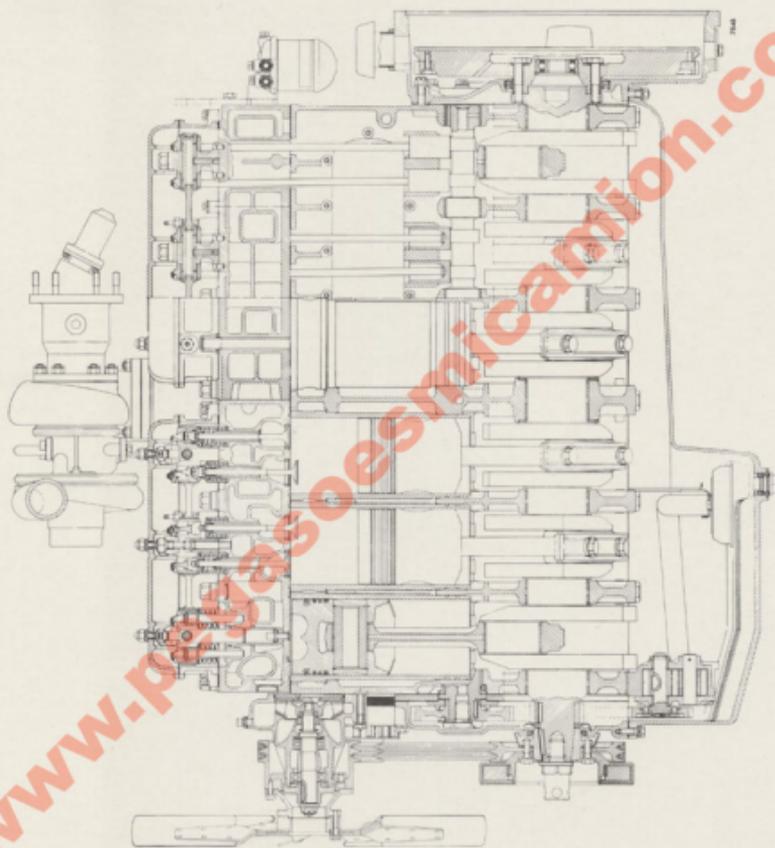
Motor 9156, sección longitudinal (Montaje DESDE)
